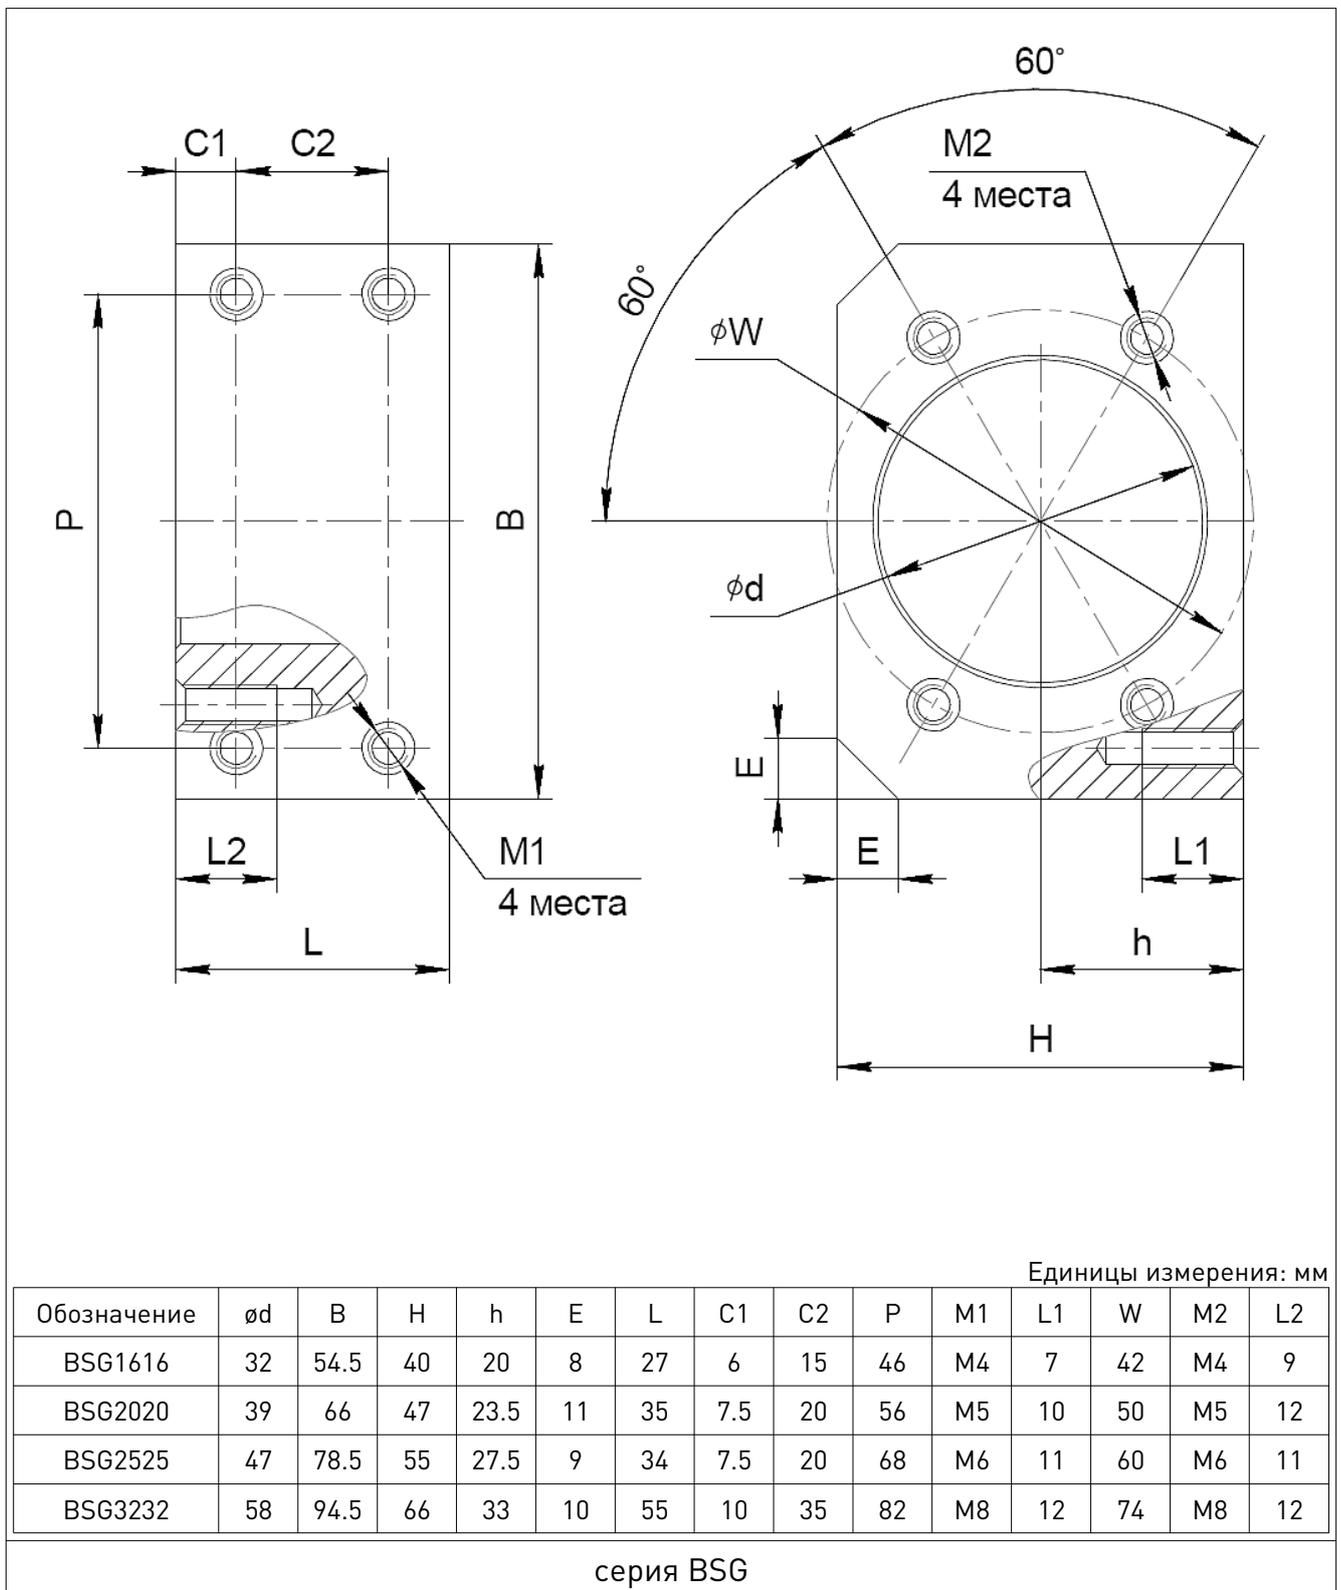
Габаритные и присоединительные размеры держателя гайки ШВП
